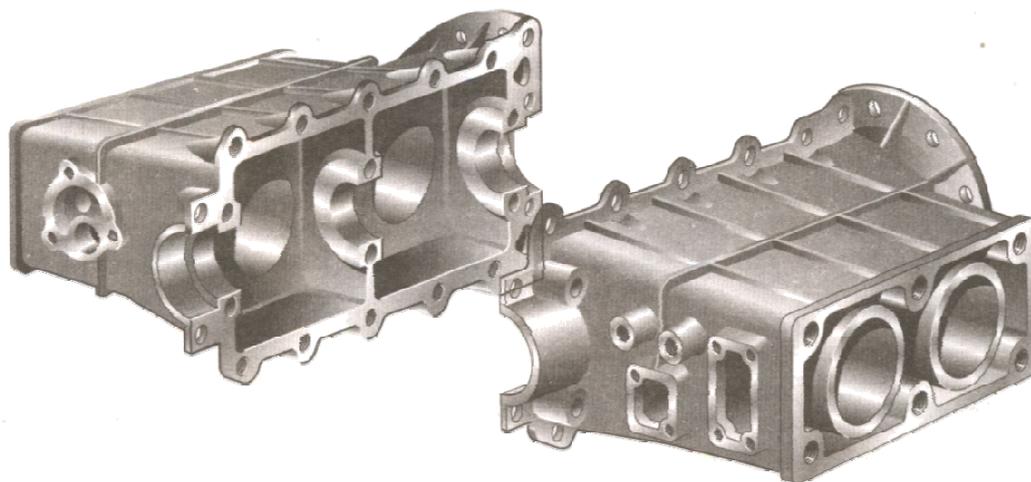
Разъемный блок-картер двигателя с оппозитным расположением цилиндров
